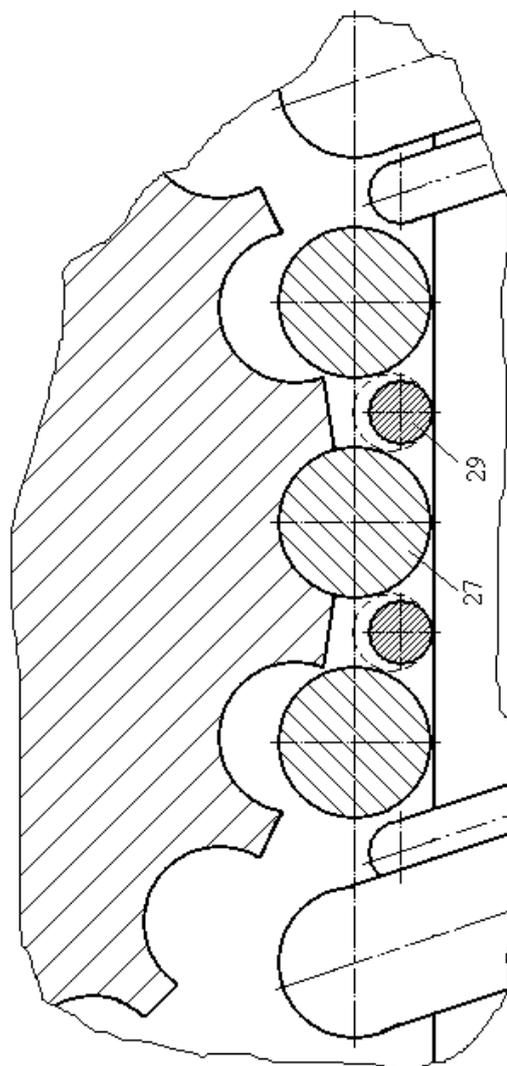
Привод с червяком в виде вала с охватывающими его двумя пружинами
